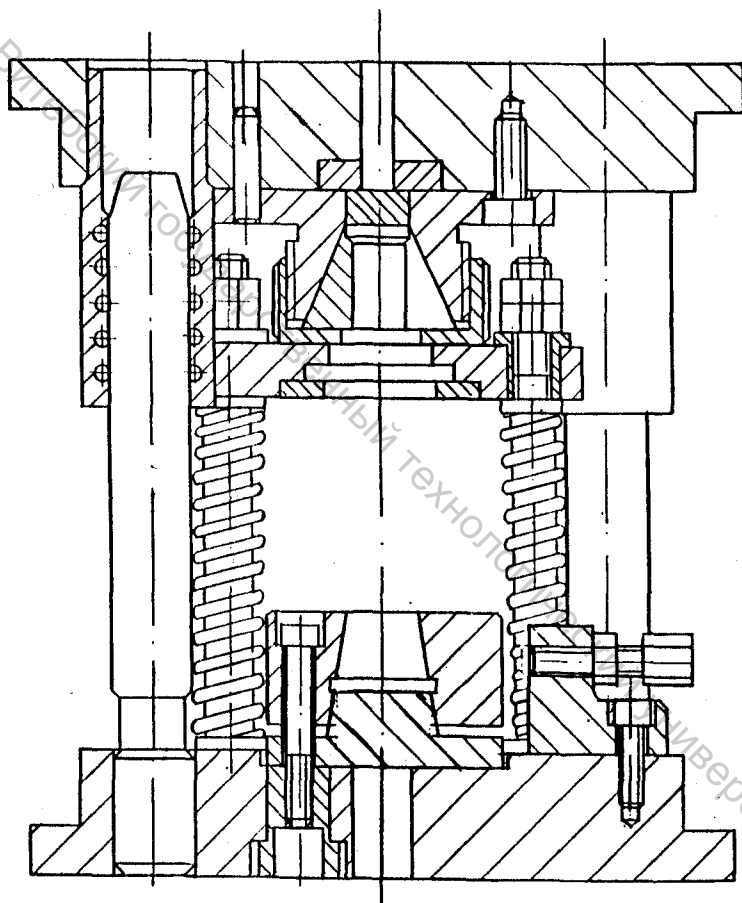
Универсальный блок с направляющими колонками для обратного выдавливания тонкостенных деталей.
